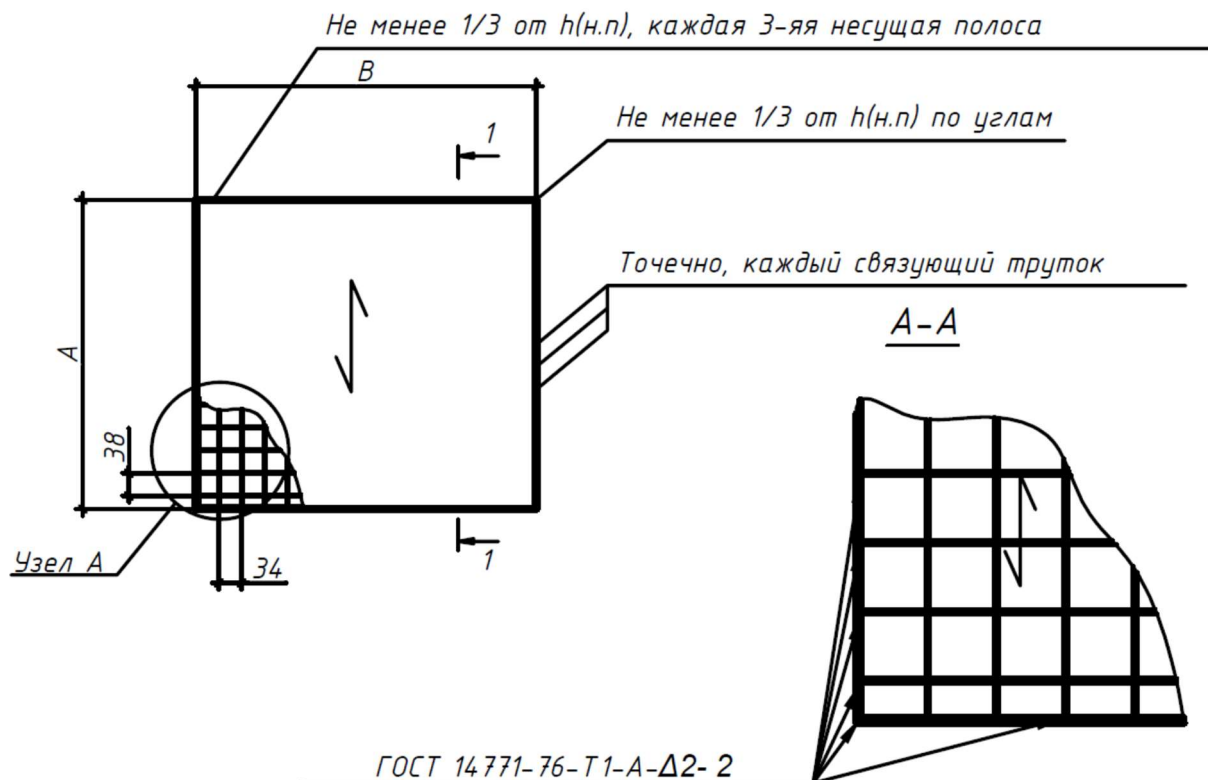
Схема приварки обрамления на щитах сварного настила
